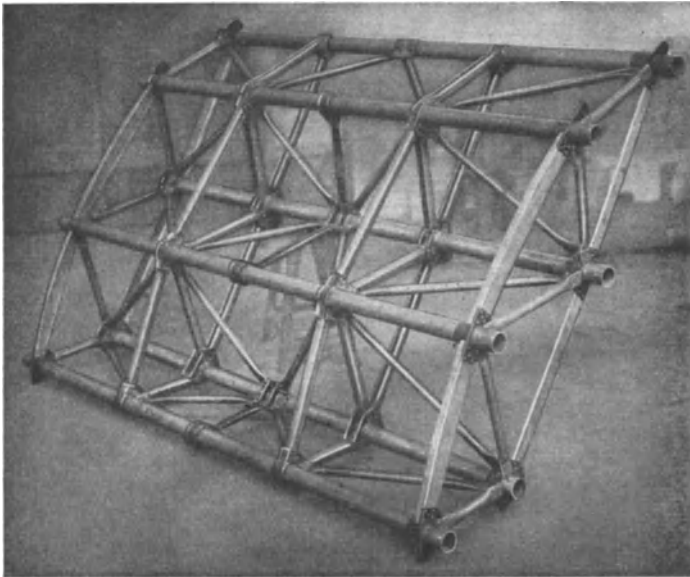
Nietanschlüsse kleiner rohrförmiger Fachwerkstreben an Holmrohre für den Flügelaufbau (Junkers).
